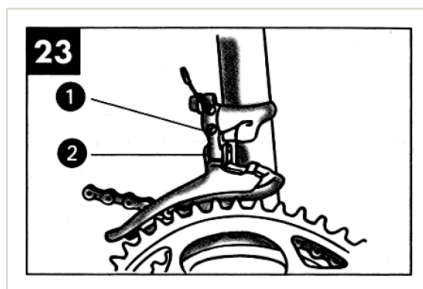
Vorderer Umwerfer: 1 Schraube a · 2 Schraube b
